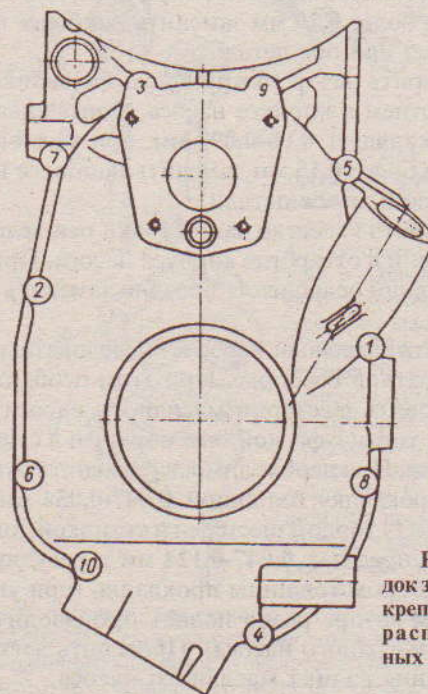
Порядок затяжки болтов крепления крышки распределительных шестерен
